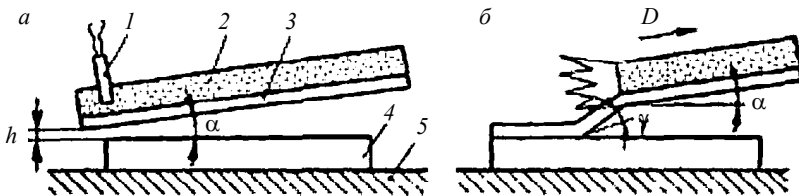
Угловая схема сварки взрывом до начала (а) и на стадии взрыва (б) [21]
